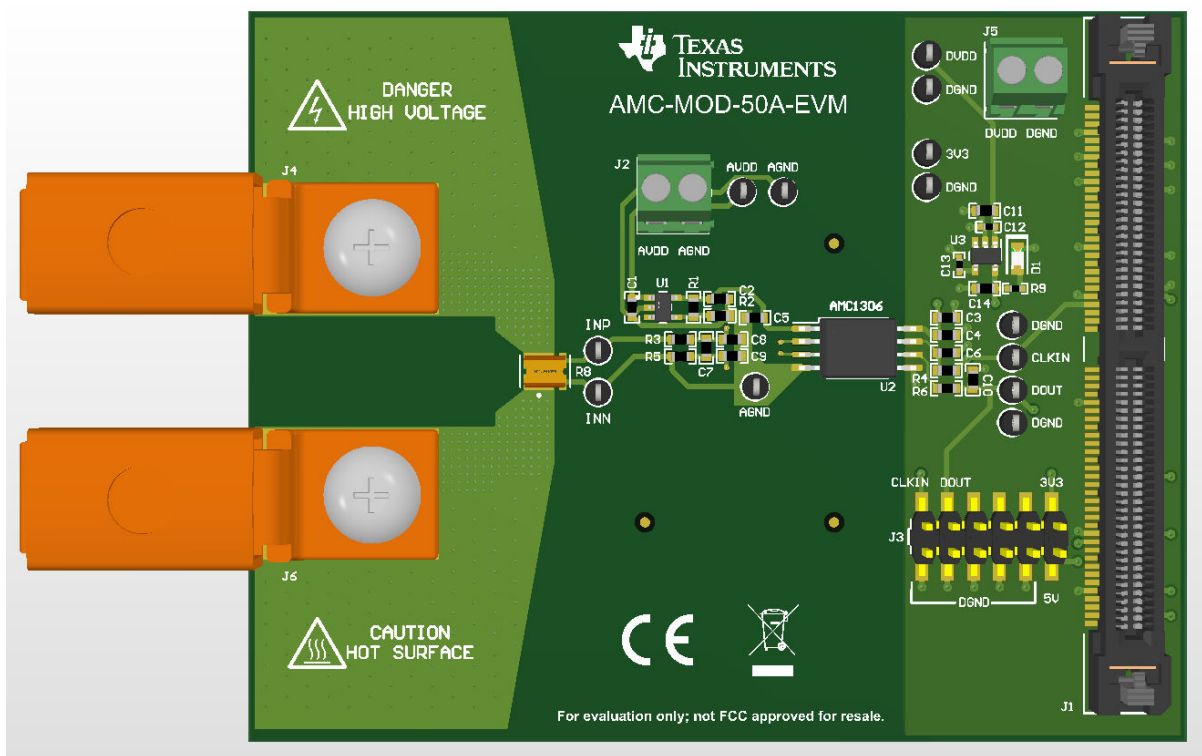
AMC-MOD-50A-EVM 顶部 PCB 图
